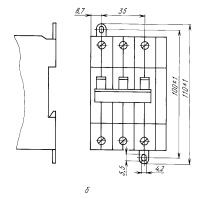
Габаритные, установочные, присоединительные размеры выключателей двухполюсных типа BA23-29 Степень защиты зажимов IP00. Масса выключателя не более 0,34 кг. Масса блока свободных контактов не более 0,05 кг
